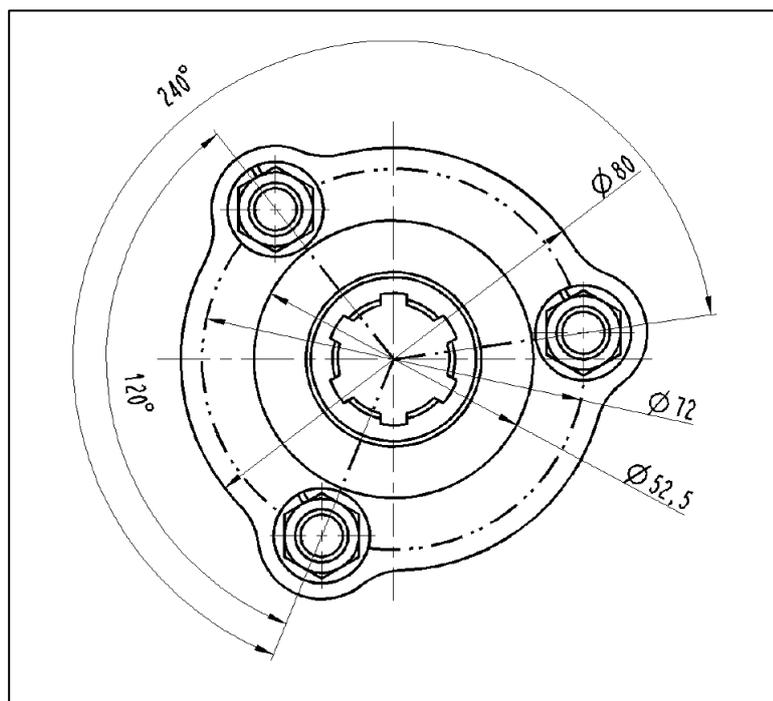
quote di collegamento kit di montaggio (2N0.800.167)
